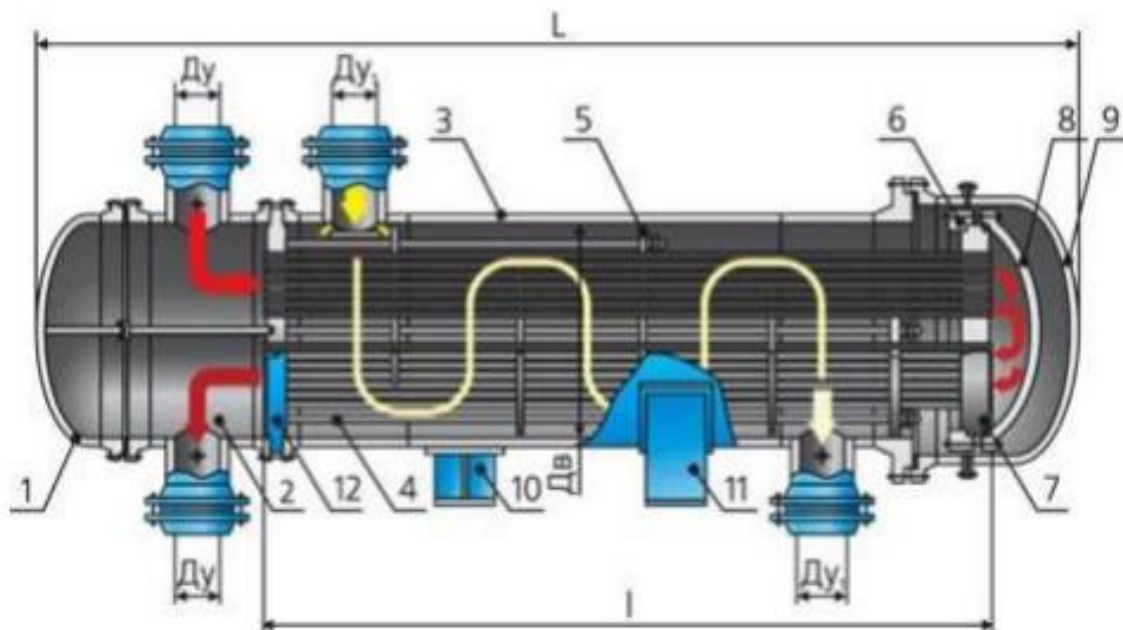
Кожухотрубчатый теплообменник с плавающей головкой:
